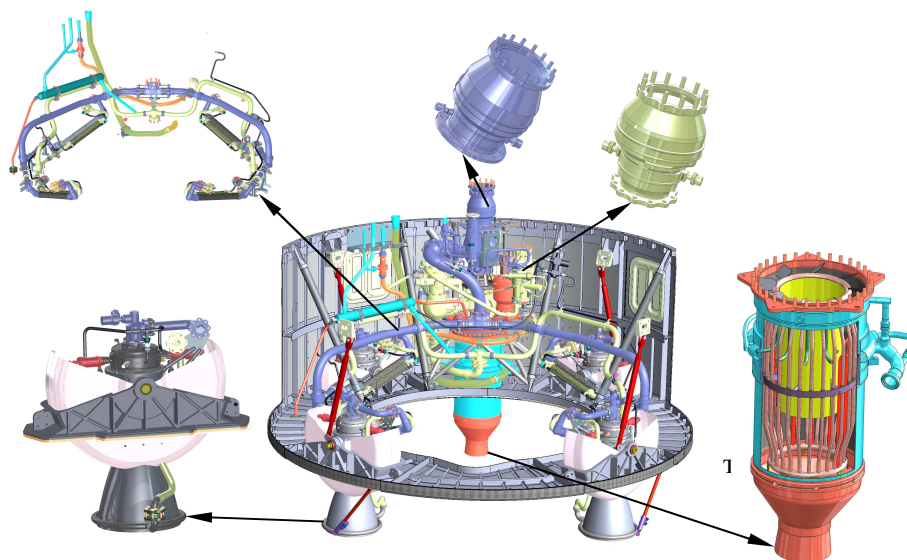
Двигатель с вновь разрабатываемыми агрегатами
